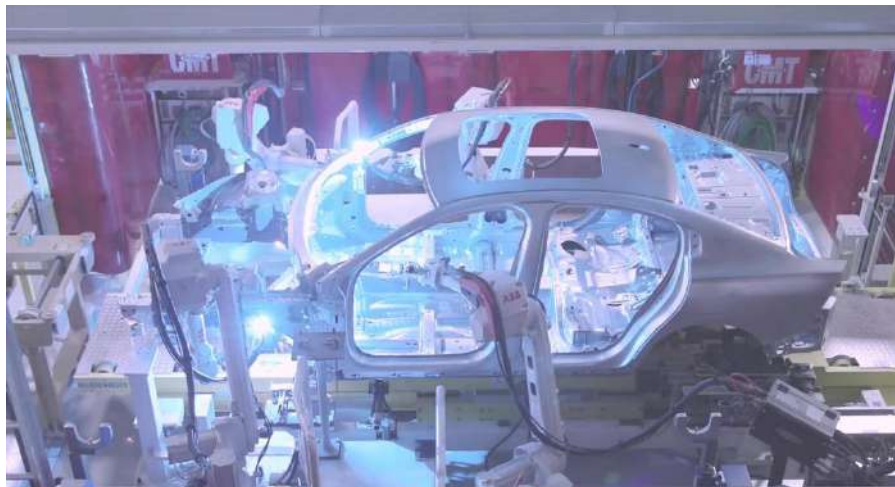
Процес зварювання роботами кузова Volvo S60
